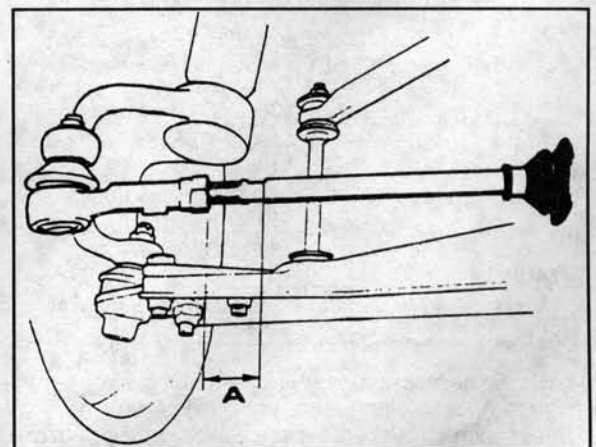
Способ проверки симметричного положения передних колес после регулировки схождения
